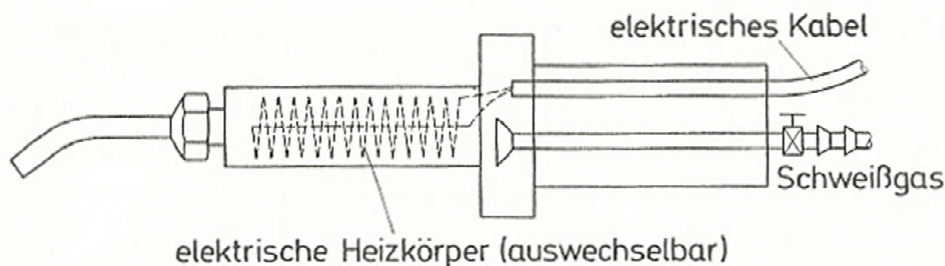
Aufbau eines Handschweißgerätes
